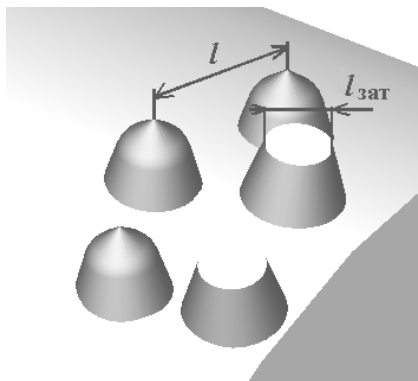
Расположение зерен на рабочей поверхности шлифовального круга
